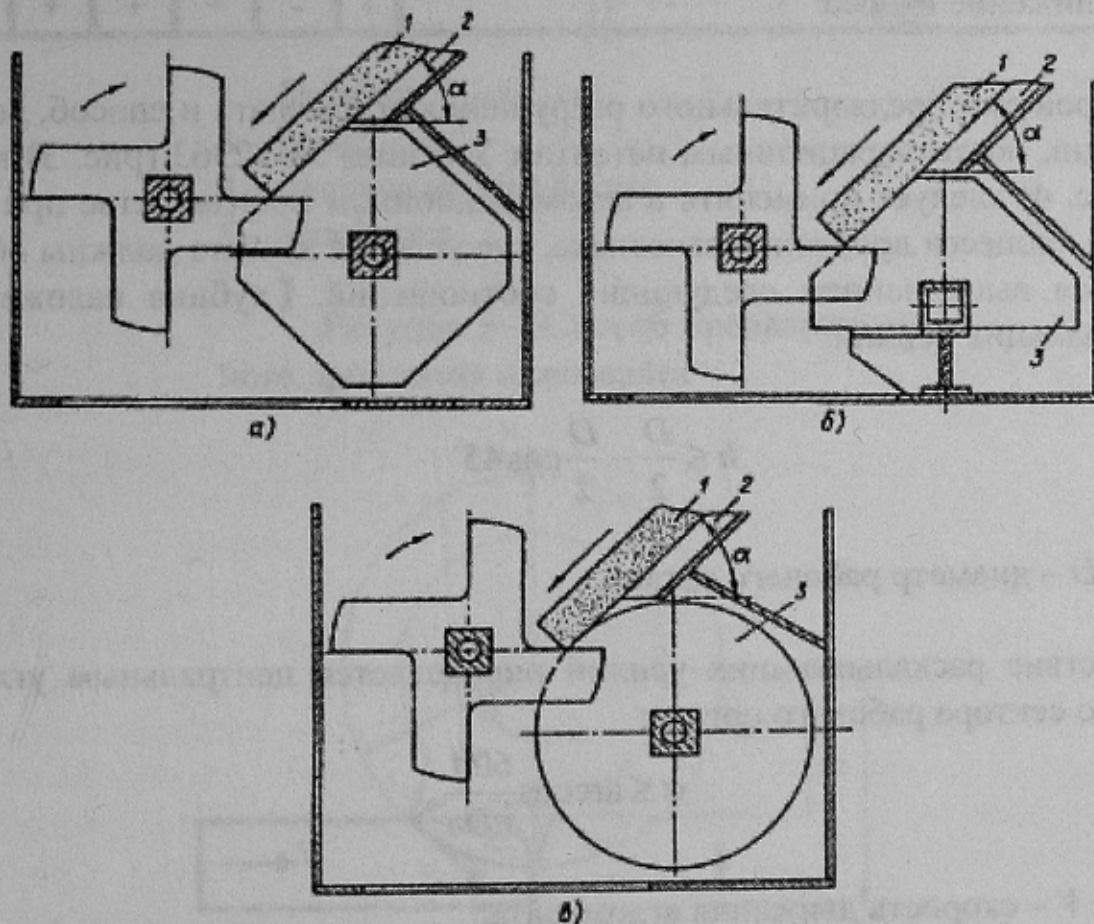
Конструктивные схемы одновалковой зубчатой дробилки с консольно расположенными колосниками: а) одновалковая дробилка с четырехпозиционными колосниками; б) одновалковая дробилка с круглыми колосниками; в) одновалковая дробилка с двухпозиционными колосниками; 1 – агломерат; 2 – на-клонная направляющая; 3 – колосники.
